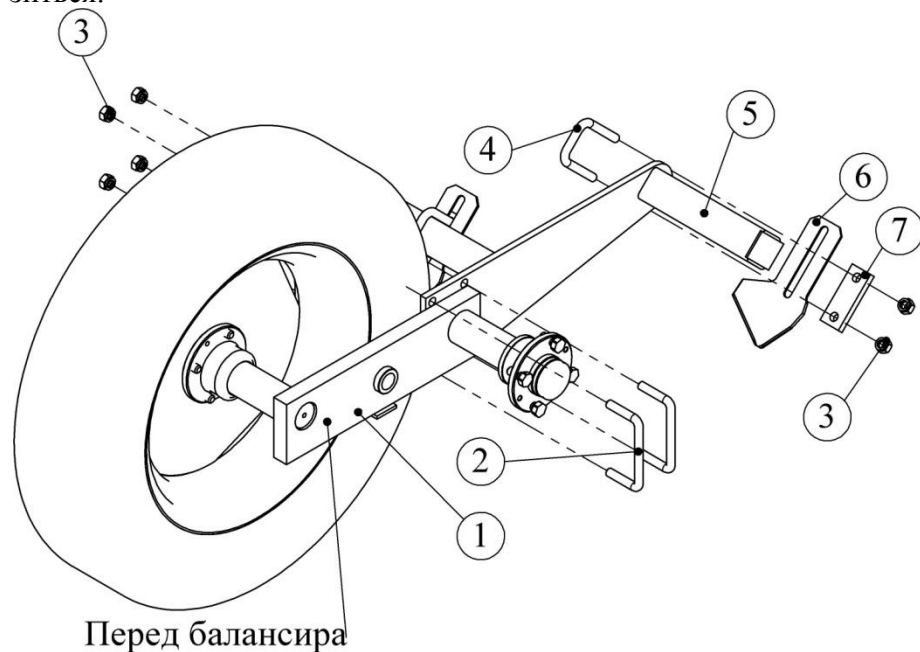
Установка чистика прикатывающего колеса.
